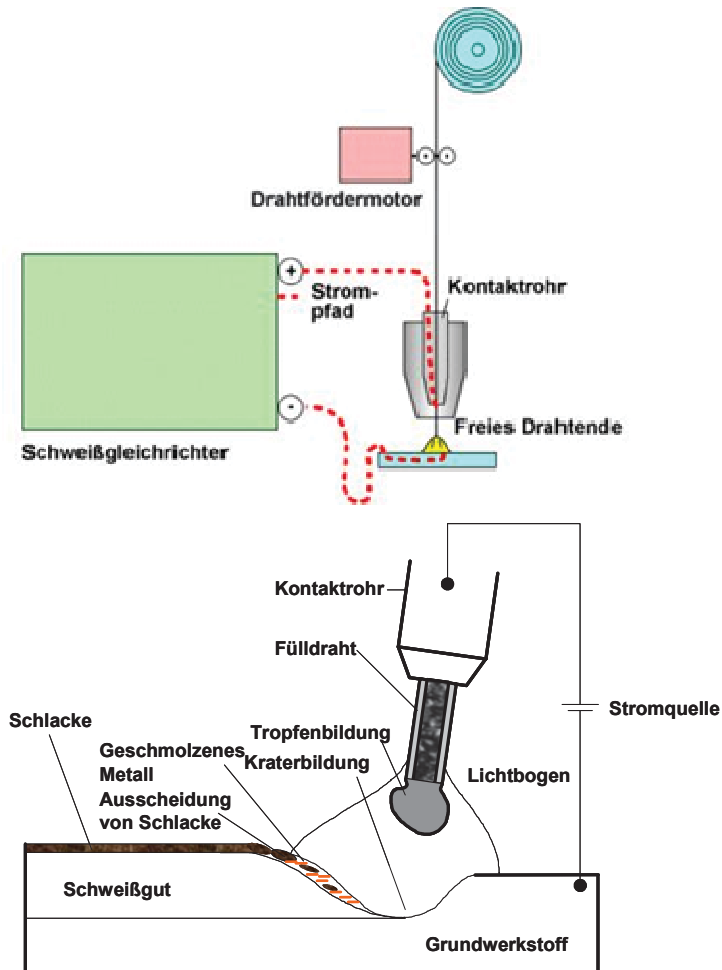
Metall Lichtbogenschweißen mit Fülldrahtelektroden ohne Gasschutz - Prozessbeschreibung
